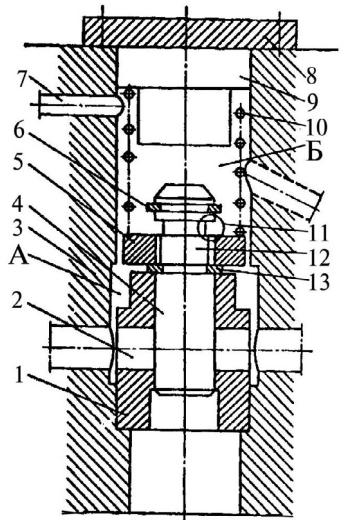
Переливний клапан плунжерного типу: 1 - корпус клапана; 2 - напірна магістраль; 3 - корпус; 4 - плунжер; 5 - поршень; 6 і 13 - упори; 7 - канал керування; 8 і 9 - кришки; 10 - пружина; 11 - виточення; 12 - канал керування.
